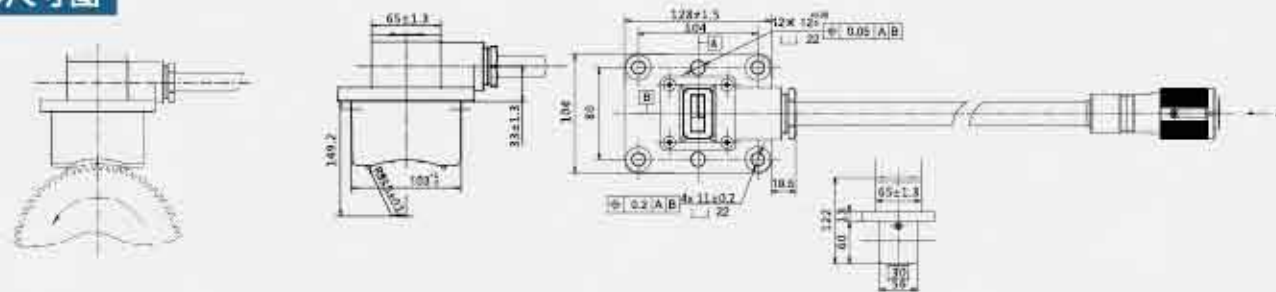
齿轮转向示意图 (顺转) 图2 外形尺寸图
